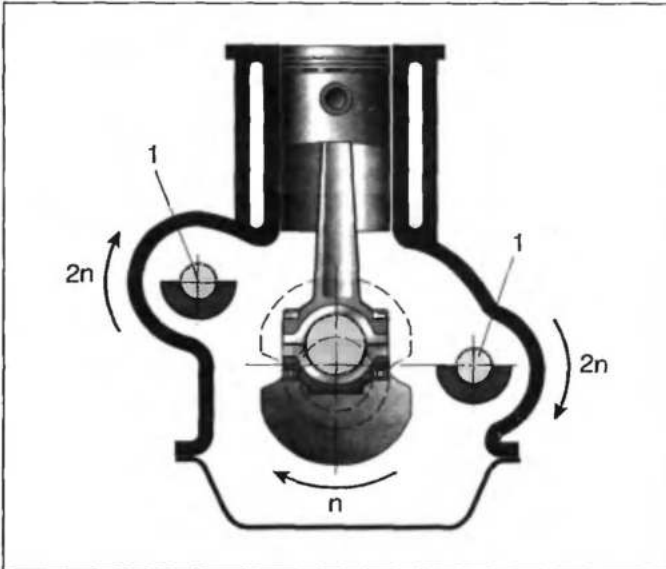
Установка балансирных валов рядного четырехцилиндрового двигателя:
